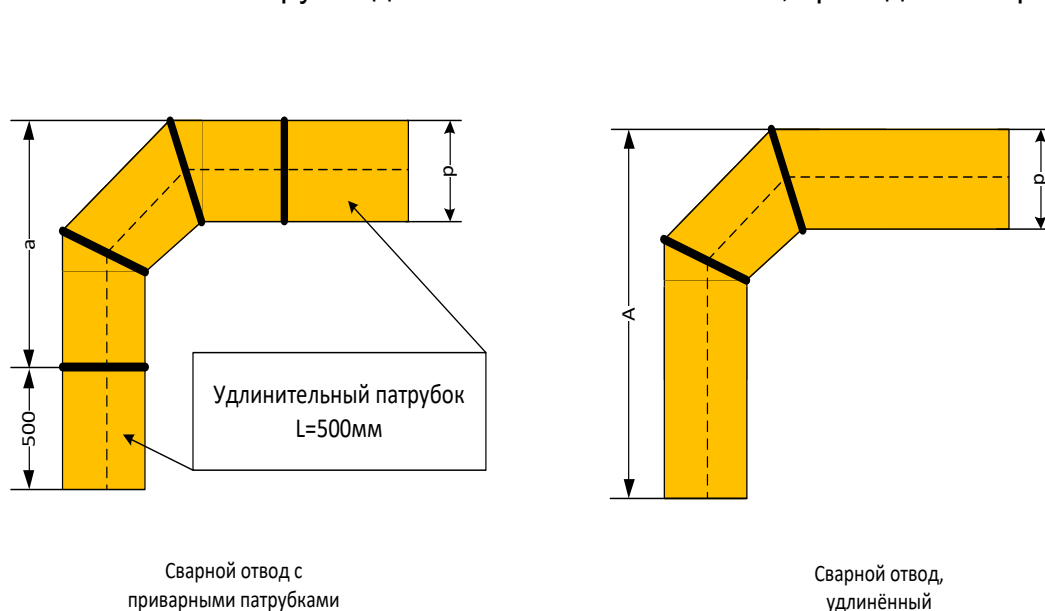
Варианты исполнения соединений полиэтиленовых труб и фитингов (Сварной отвод с приваренным патрубком)
